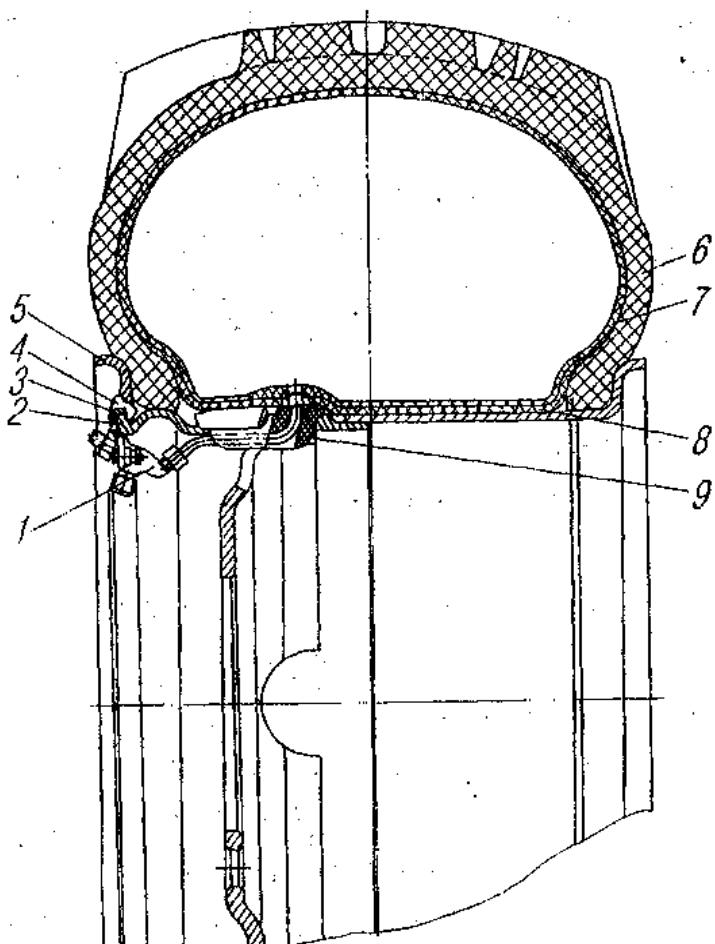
Колесо с шиной в сборе: 1-кран колесный; 2-основание обода с диском; 3-ограничитель замочного кольца; 4-кольцо замочное; 5-кольцо бортовое; 6-покрышка; 7-камера; 8-лента ободная; 9-уплотнитель вентильного паза
